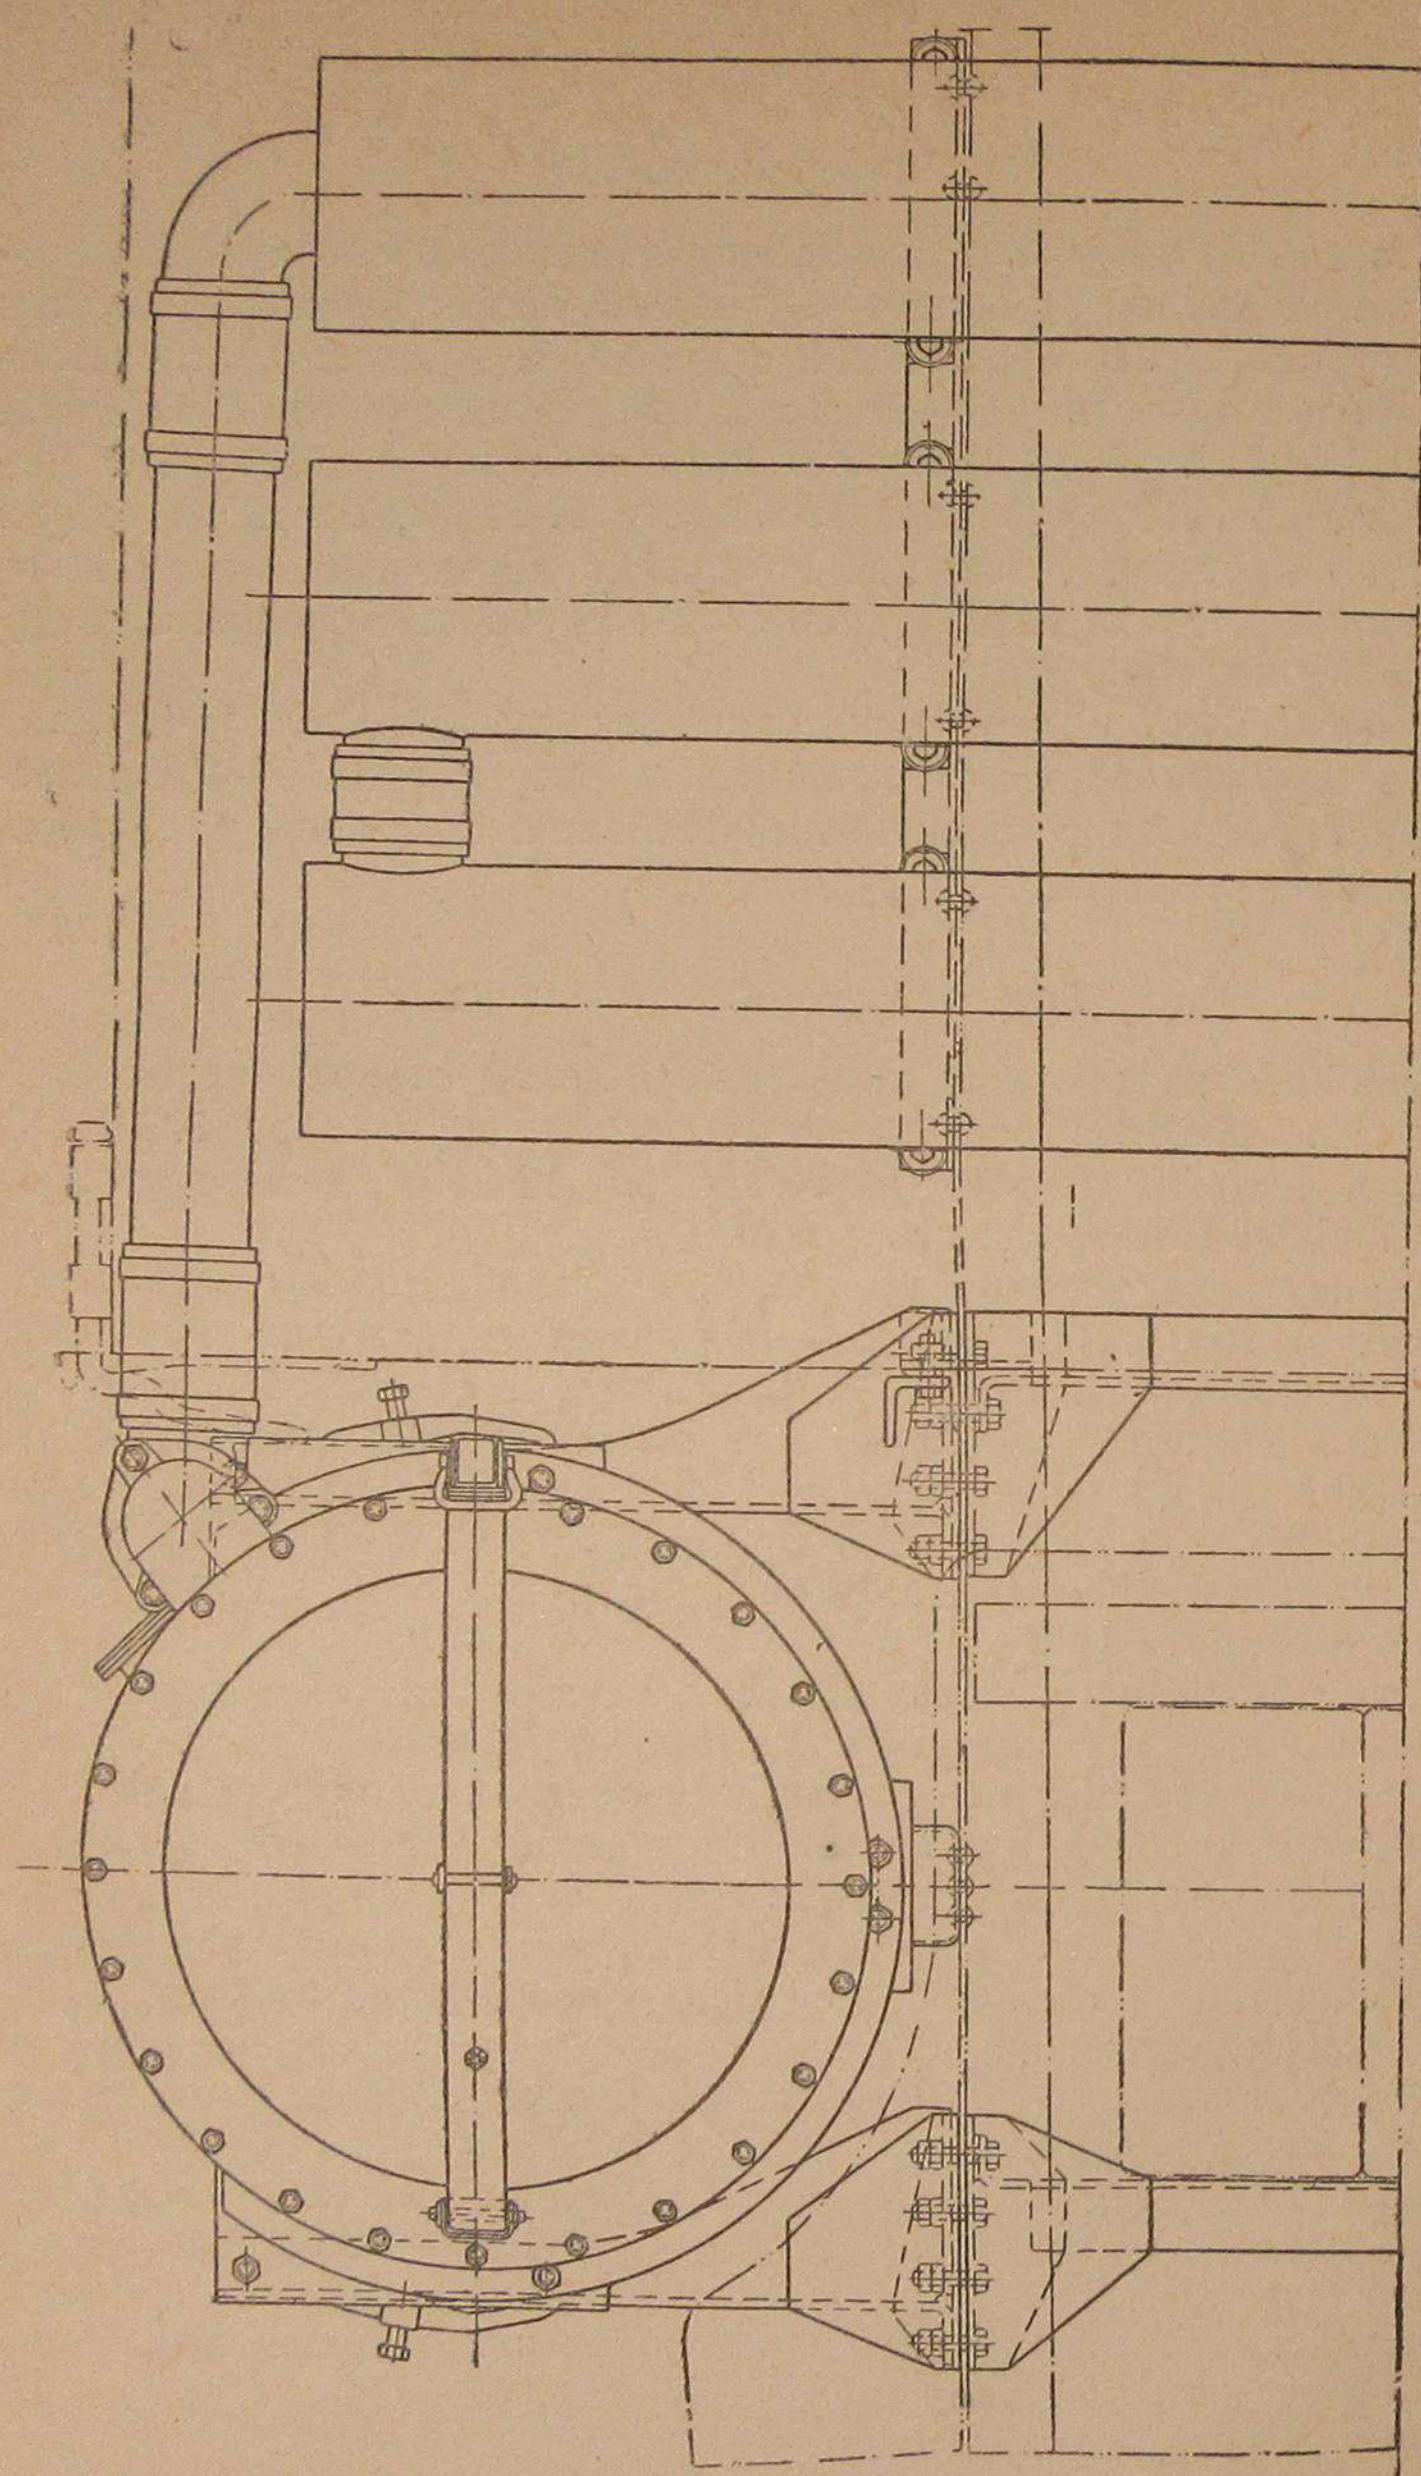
Общий вид сверху установки и крепления газогенератора ЗИС-21
